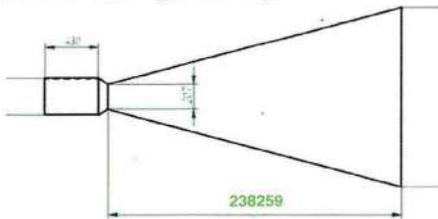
Dimensiones tobera del motor cohete de combustible líquido.
